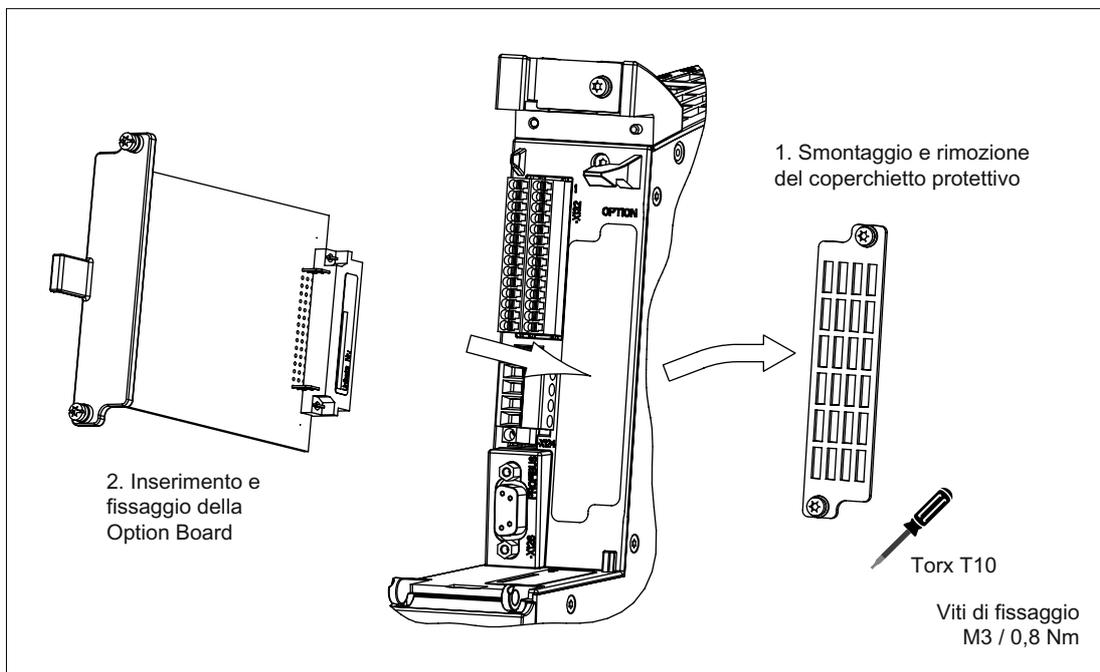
Montaggio della Option Board in una CU320-2 DP
